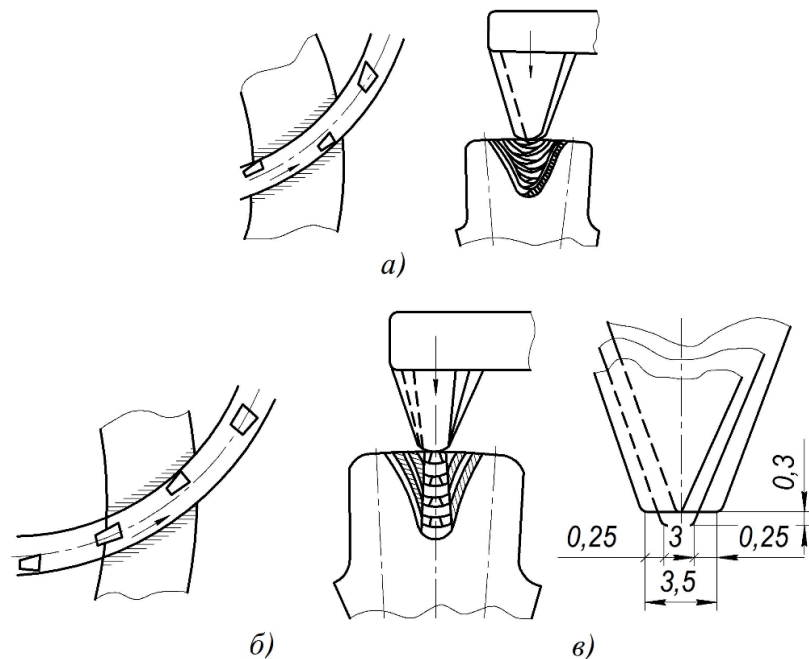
Нарізування конічного зубчастого колеса з криволінійними зубами:
